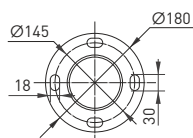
Чертеж и габаритные размеры фланца OXOR-OK2-D108
